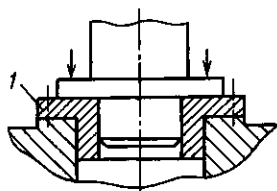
Схема установки заготовок наружной цилиндрической и плоской торцевой поверхностями во втулку 1
